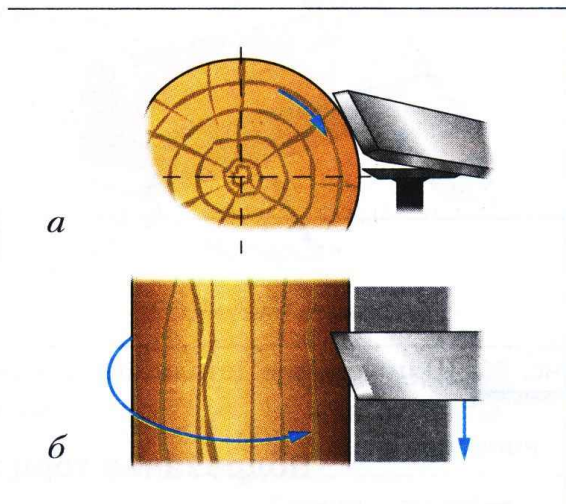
Чистовое точение косой стамеской: а — вид с торца заготовки; б — вид сверху
